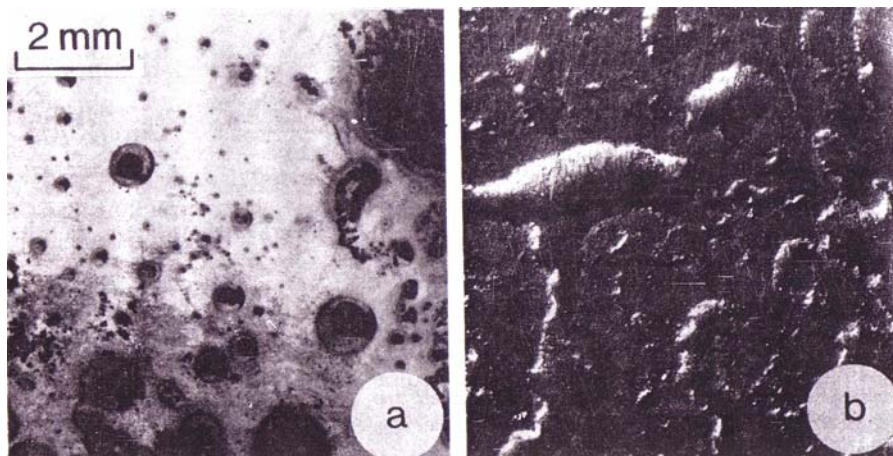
Condiciones de mojado por soldadura (a) y desmojado (b)
